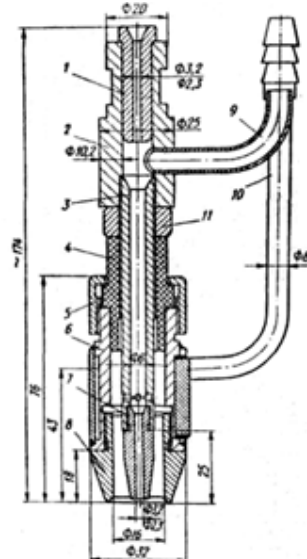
Газоэлектрическая горелка для автоматической сварки в среде углекислого газа с принудительным водяным охлаждением: 1 — вставка стальная сменная; 2 — втулка бронзовая; 3 — трубка токоподводящая; 4 — втулка изоляционная; 5 — гайка накидная; 6 — корпус горелки; 7 — мундштук токоподводящий; 8 — сопло; 9 — трубка для подвода защитного газа; 10 — трубка для подвода охлаждающей воды в горелку; 11 — гайка специальная
